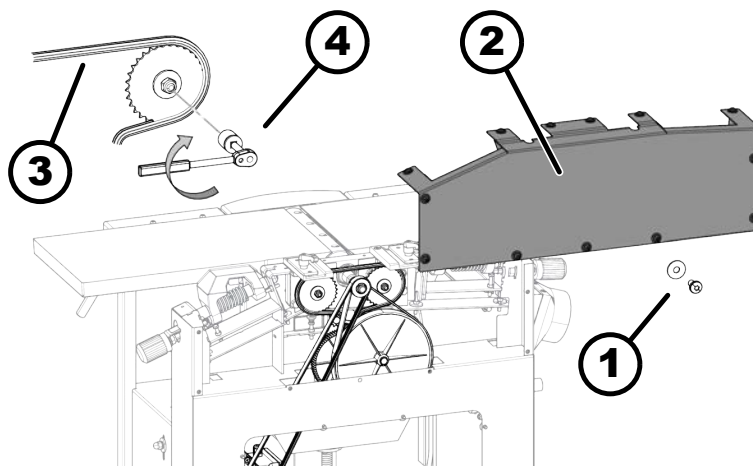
Engrasar la cadena de transmisión de los rodillos de transporte
